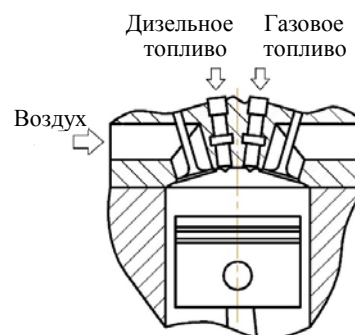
Газодизель с двумя форсунками для подачи дизельного и газового топлива
